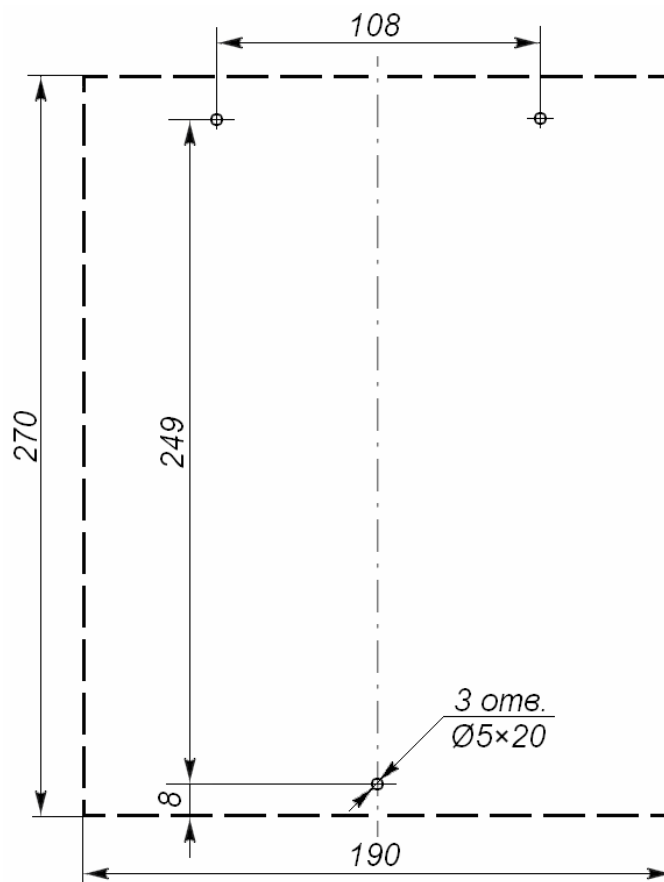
Разметка отверстий в стене для крепления блока управления
